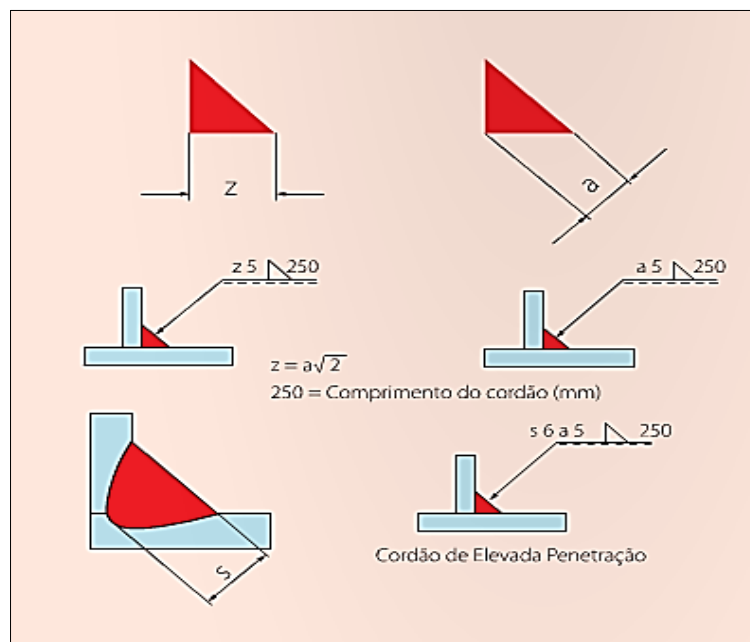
Representação das dimensões do cordão segundo a norma Iso 2553 e AWS (z-cateto da soldadura, a- altura da soldadura e s- soldadura + penetração)
